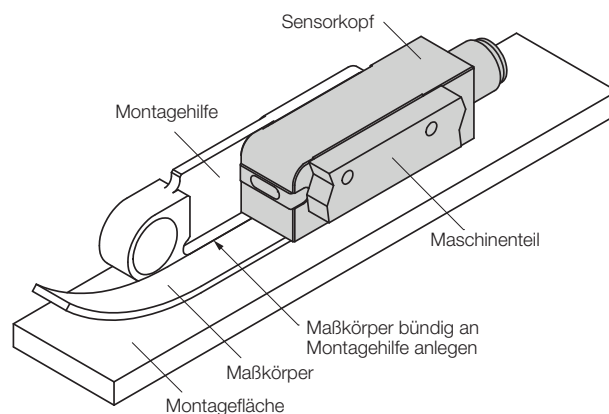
Montagehilfe BAM TO-ML-006-S1G (Bestellcode BAM0256) befestigen (Links- oder rechtsseitige Befestigung ist möglich, Abbildung zeigt rechtsseitige Befestigung)
